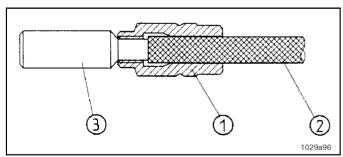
Предварительный монтаж резьбовых гильз с помощью установочного калибра
